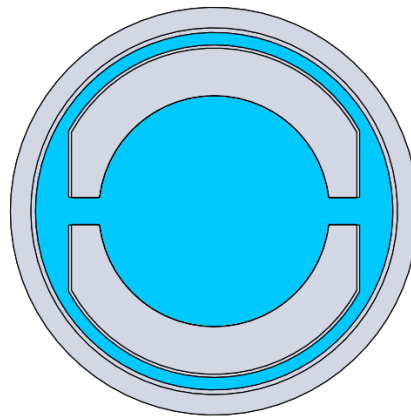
Imagen del CAD de la pieza 9, en color gris, y del soporte, en color azul, tras realizar su diseño mediante el escalado y la operación booleana de corte antes de realizar su arreglo.
